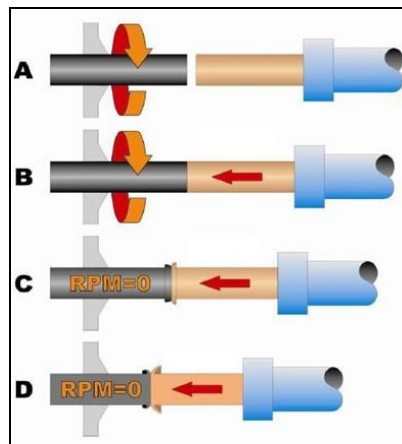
b – Etapas do processo de soldagem por atrito contínuo:
